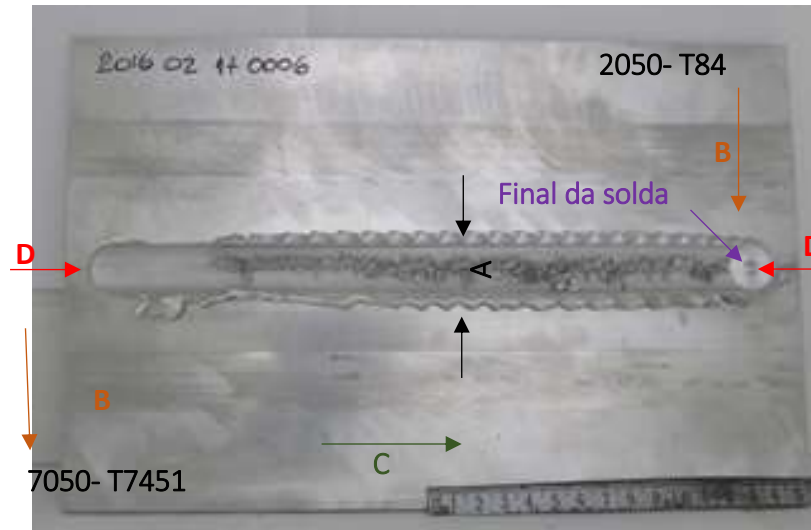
Junta de topo das ligas dissimilares de alumínio-lítio 2050-T84 e alumínio 7050-T7451 soldadas por FSW.
